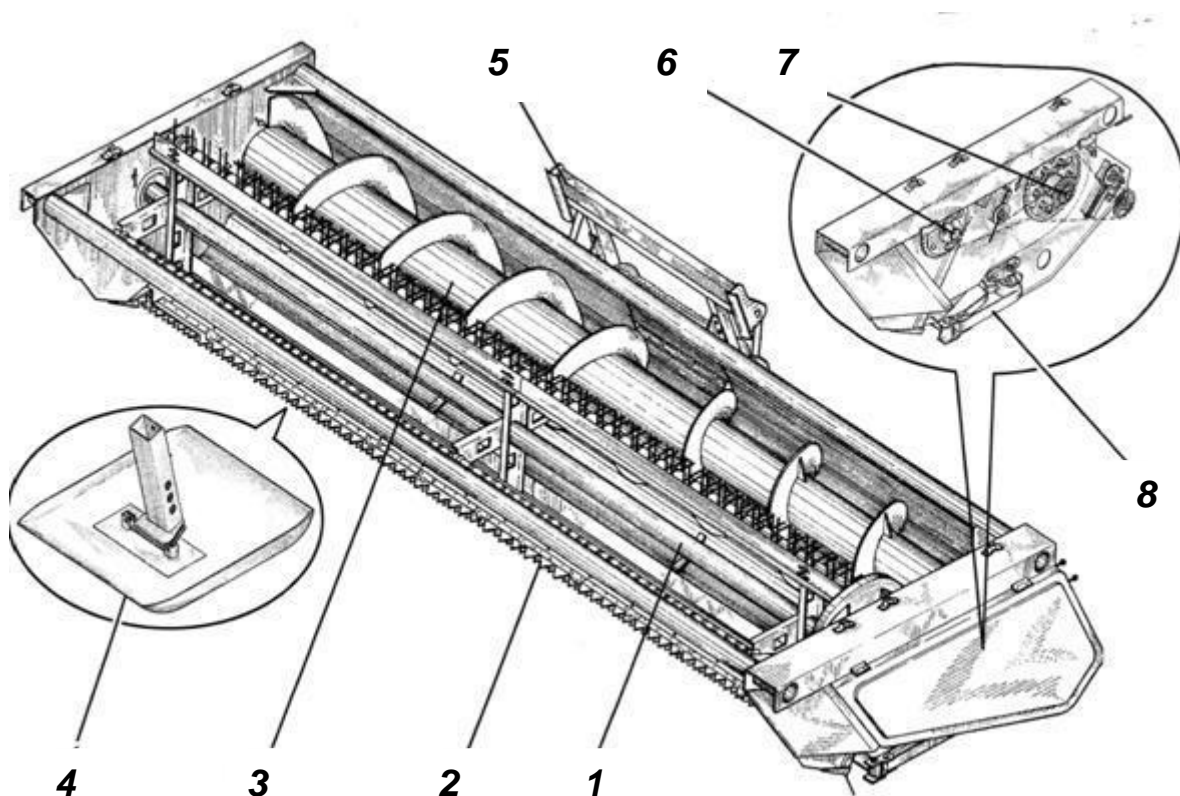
Жатка для уборки трав: 1 – мотовило; 2 – режущий аппарат; 3 – шнек; 4 – башмак; 5 – проставка; 6, 7 – устройство предохранительное; 8 – колебатель
